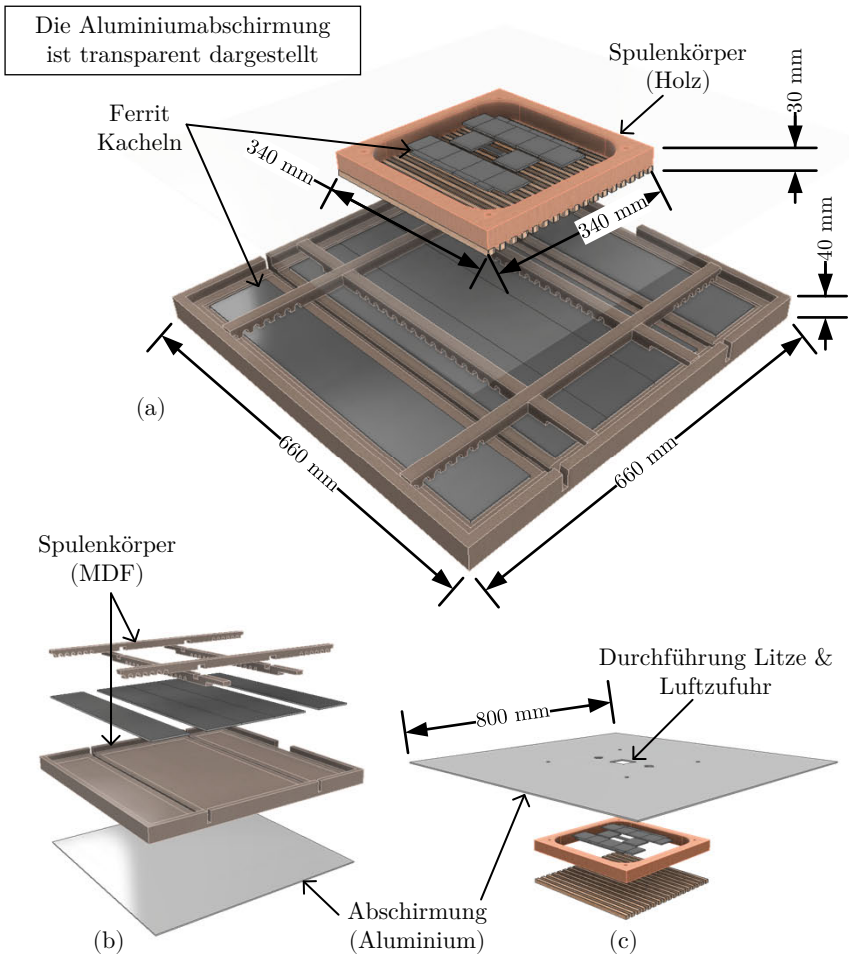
(a) CAD-Konstruktion der Spulenkörper mit Ferritspiegel und Abschirmungen. (b) Explosionszeichnung des GA-Spulenkörpers. (c) Explosionszeichnung des VA-Spulenkörpers. Die Aluminiumplatte besitzt Löcher für die Durchführung der Anschlüsse und für Luftzufuhr zur Kühlung der Wicklung.
